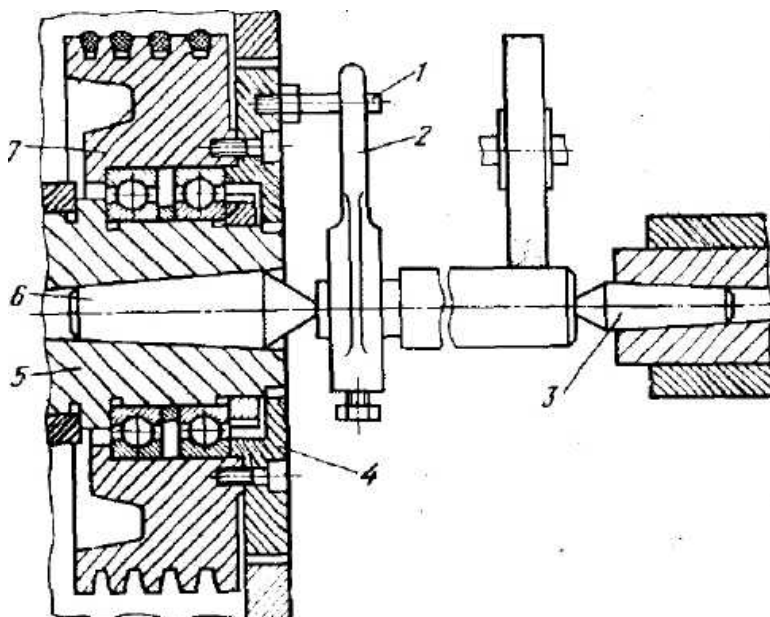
Схема установки заготовки в центрах: 1— поводковый палец; 2— хомутик; 3— задний упорный центр; 4— поводковый диск; 5— шпиндель передней бабки станка; 6— передний упорный центр; 7— шкив.
